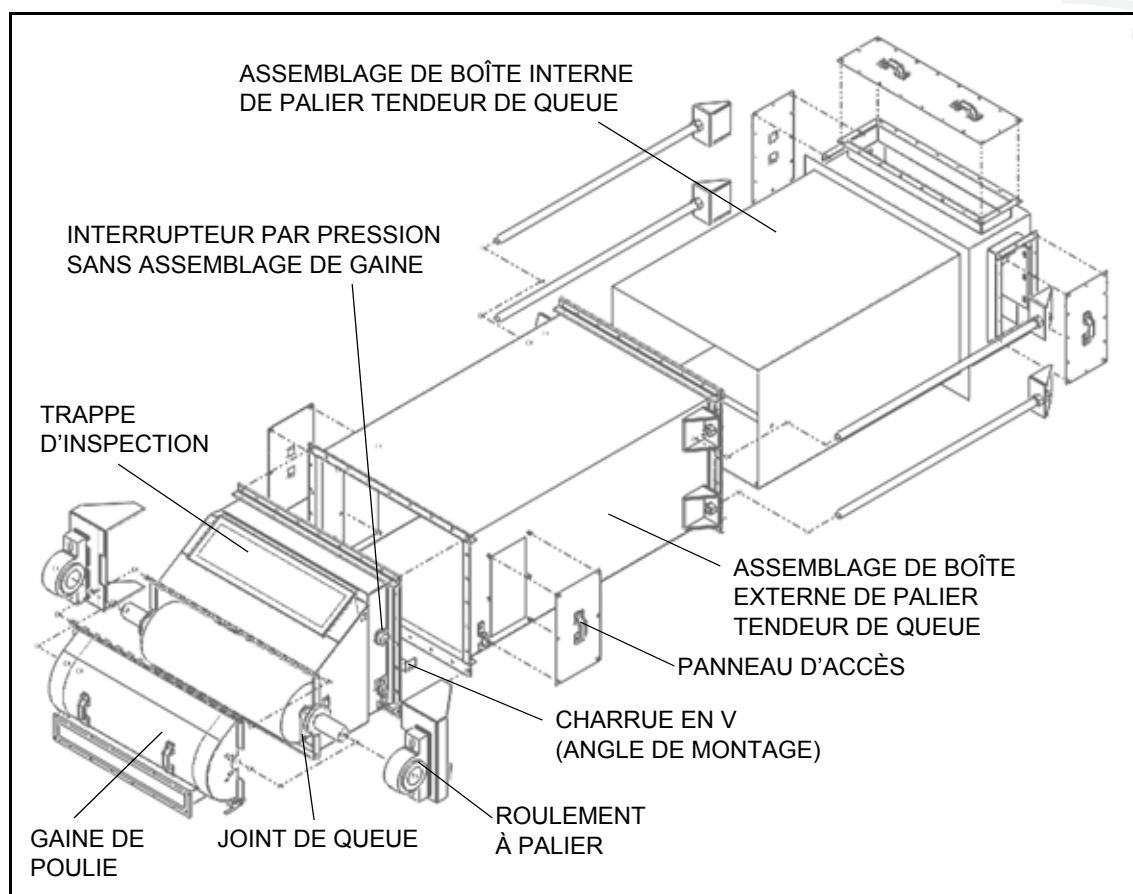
Vue éclatée de la section de queue avec palier tendeur à vis
